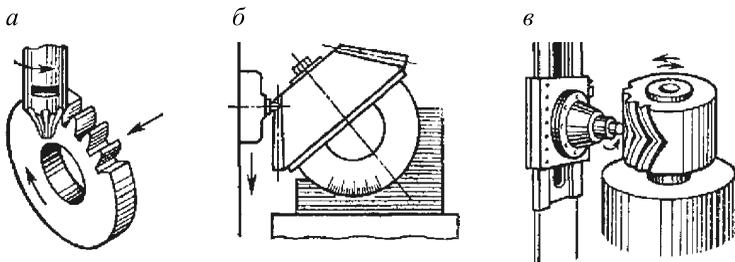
Схемы нарезания пальцевыми фрезами зубьев колес
